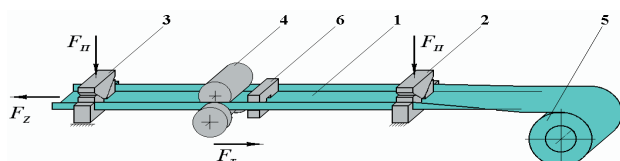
Способ изготовления профилей в непрерывно-циклическом режиме
